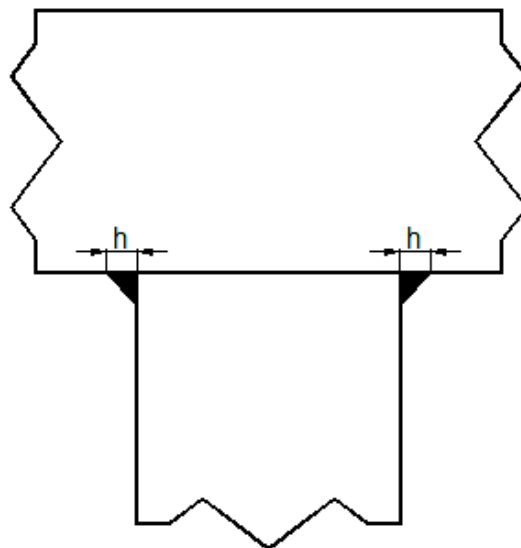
Soldadura del vertical en la parrilla
